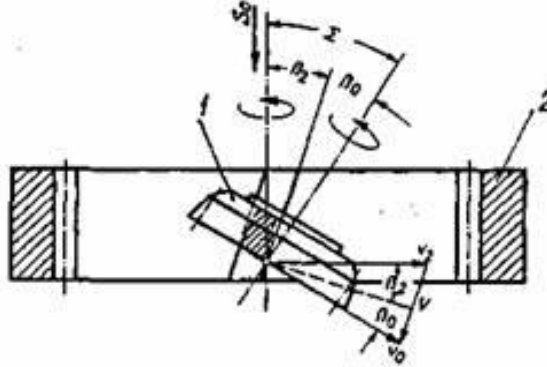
Схема зуботочения цилиндрических колес с внутренним зацеплением
